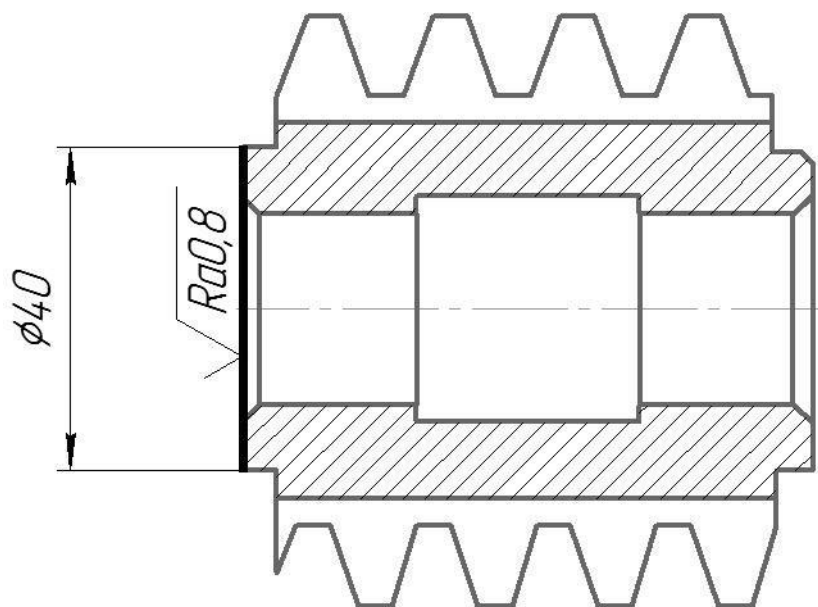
Ескіз деталі з вимогами до якості обробленої поверхні
